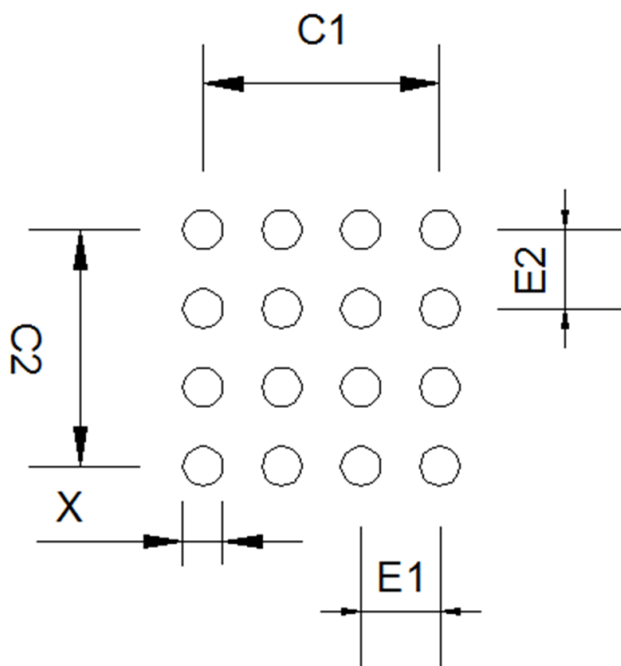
CSP16 PCB 焊盘布局图
